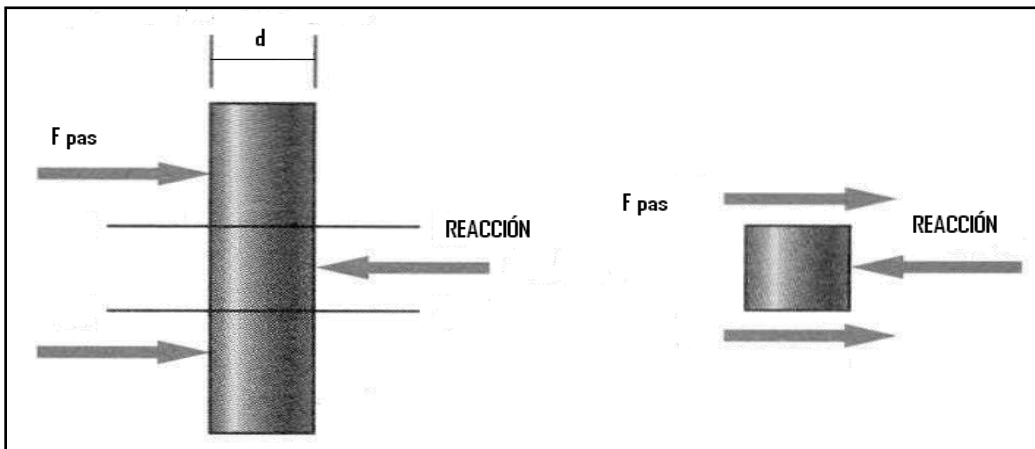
Corte doble en un pasador. Fuente: Beer, Johnston, Dewolf. Mecánica de Materiales.
